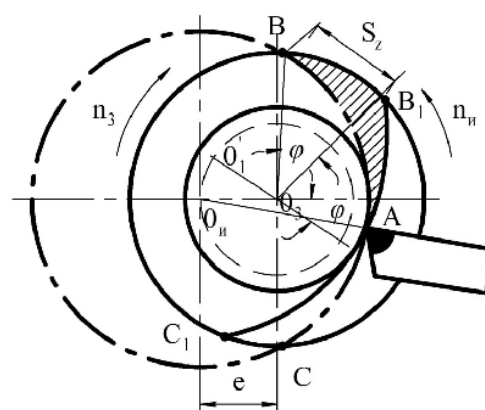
Схема движения при внутреннем касании инструментальной головки с обрабатываемой поверхностью заготовки
